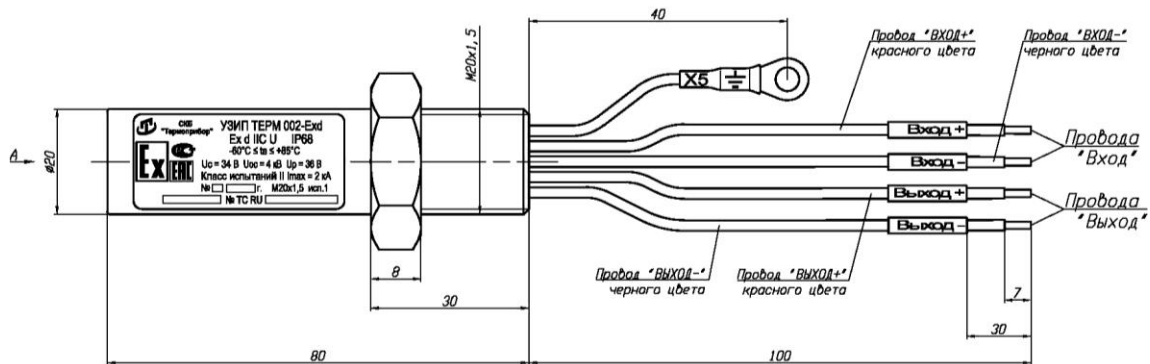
Габаритный чертёж УЗИП ТЕРМ 002 G3/4
